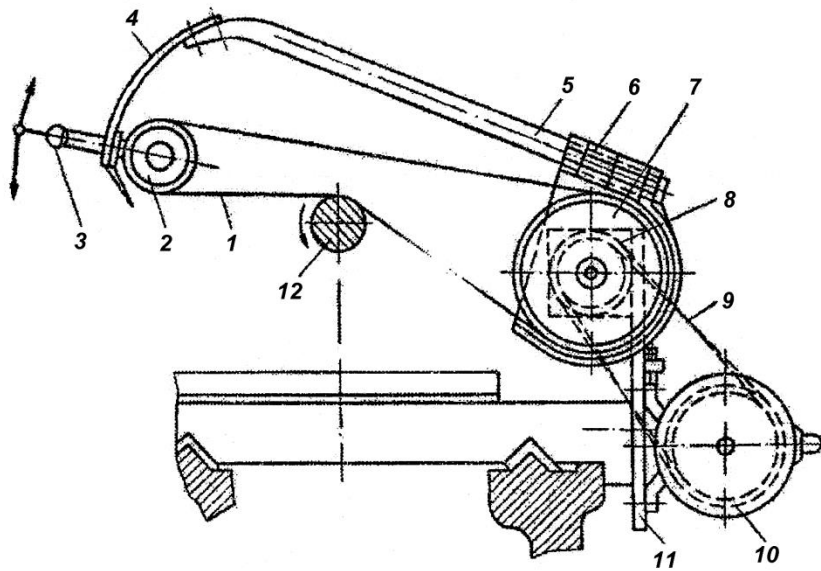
Схема пристрою для полірування деталей безкінечною стрічкою.
